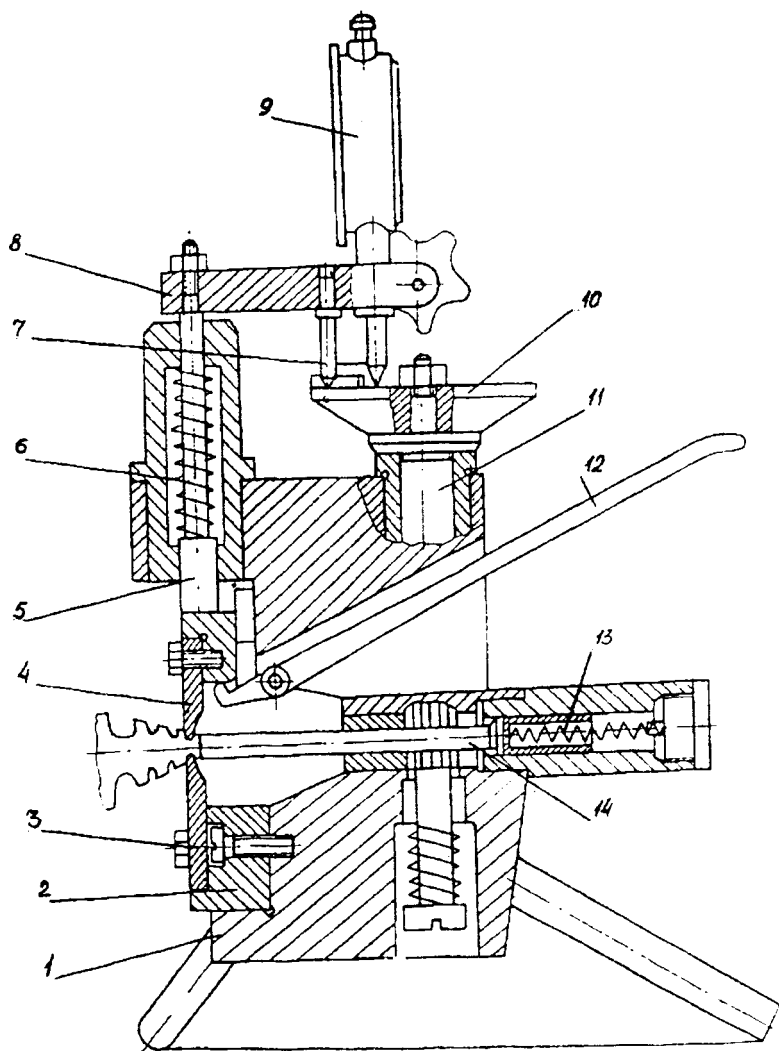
Приспособление для контроля размеров елочного замка лопатки по роликам
